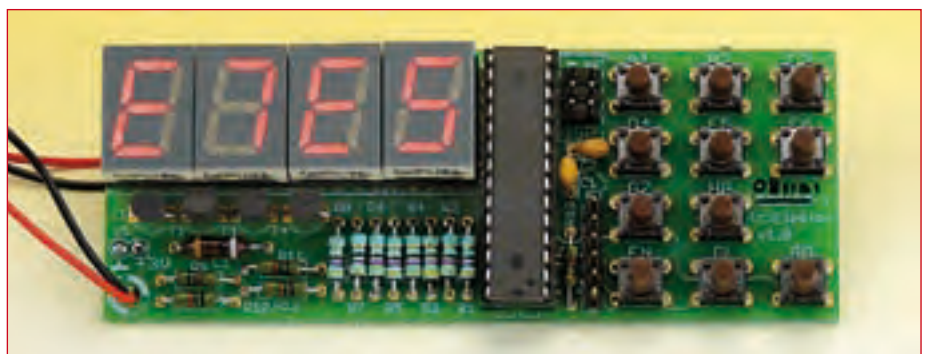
Tarjeta completamente montada del mini-ajedrez AVR.
